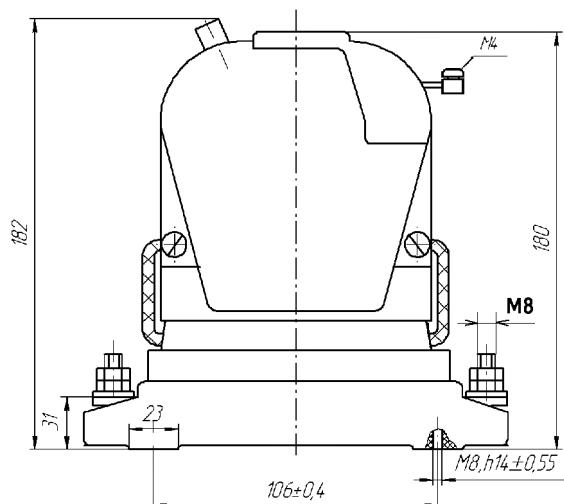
Габаритные, установочные и присоединительные размеры реле типа ТРТП-150.
